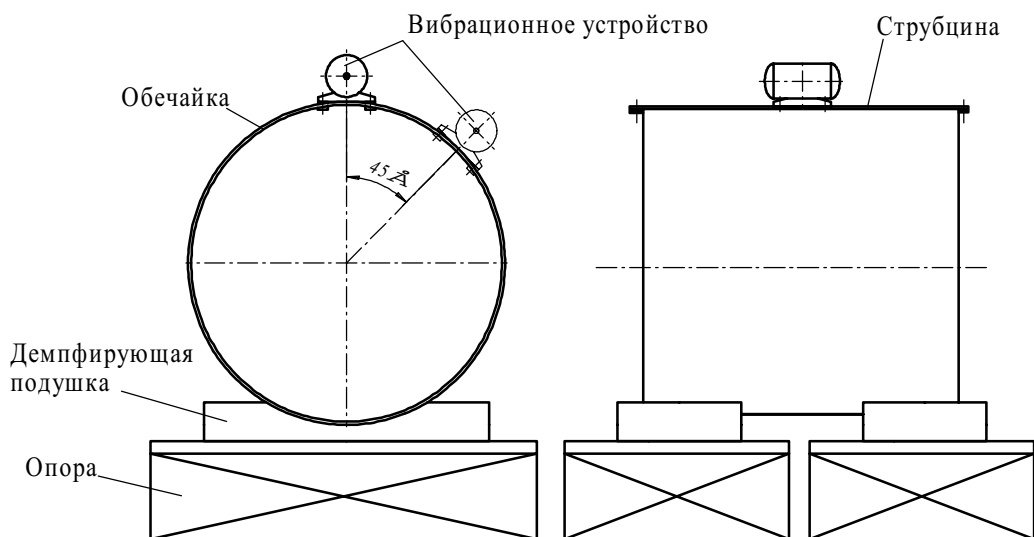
Схема конструкции установки для вибрационной обработки базовых деталей корпусов аппаратов
